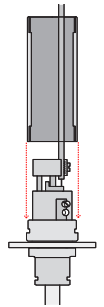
zu Schritt 8: Verbinder mit Gehäuse
